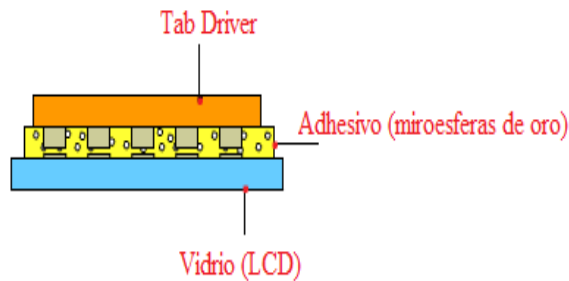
Tab Driver encapsulado y sellado. Fuente: Hitachi-Chem [3].
